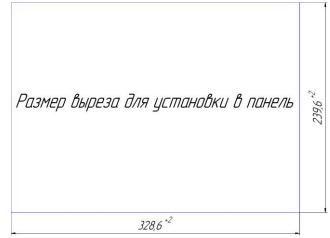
Установочные размеры для крепления в панель(щит)
